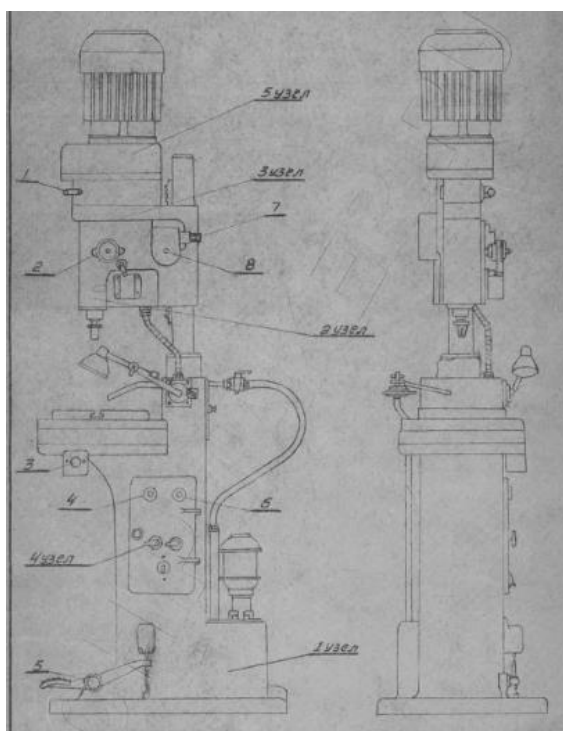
Вертикальный резьбонарезной станок модели 5053
